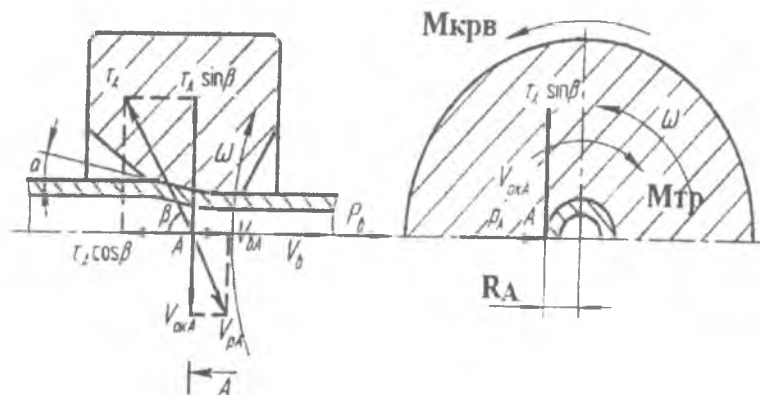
Напряжения трения и скорости движения в канале вращающейся волоки на границе контакта поверхностей инструмент-заготовка
